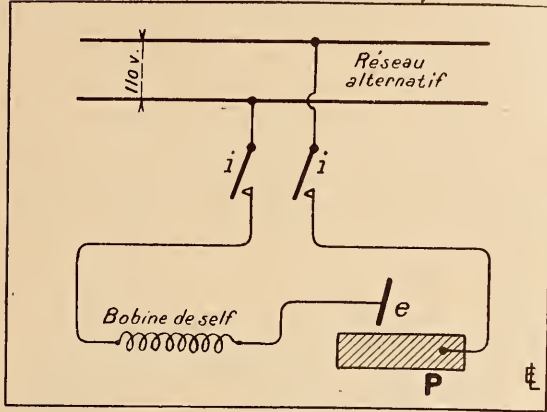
Poste de soudure avec bobine de réactance.
